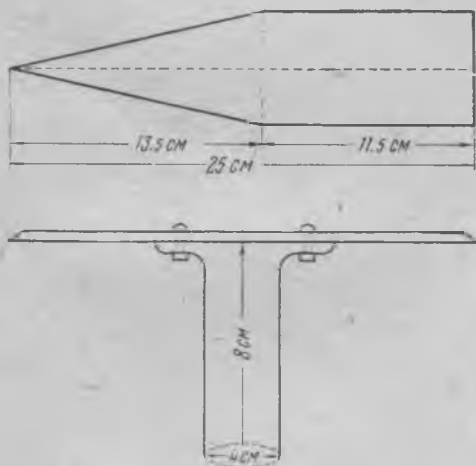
Мотыжка для рыхления корки на питомниках при грядковом посеве (конструкции В. И. Скорб)
